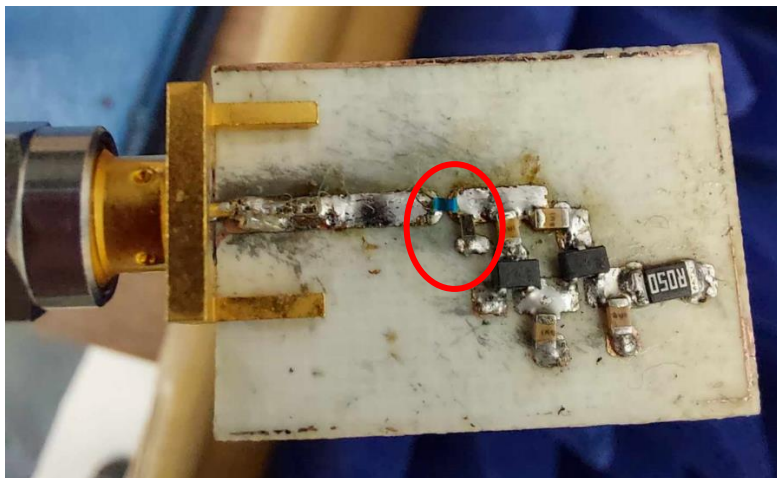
Rectificador con red de acoplamiento y componentes soldados.
